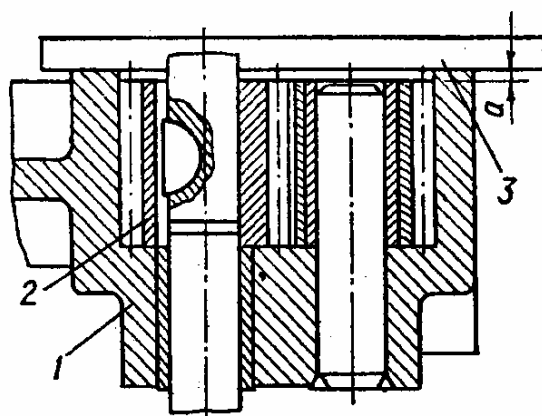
Перевірка торцевих зазорів між шестернями і корпусом масляного насоса:
